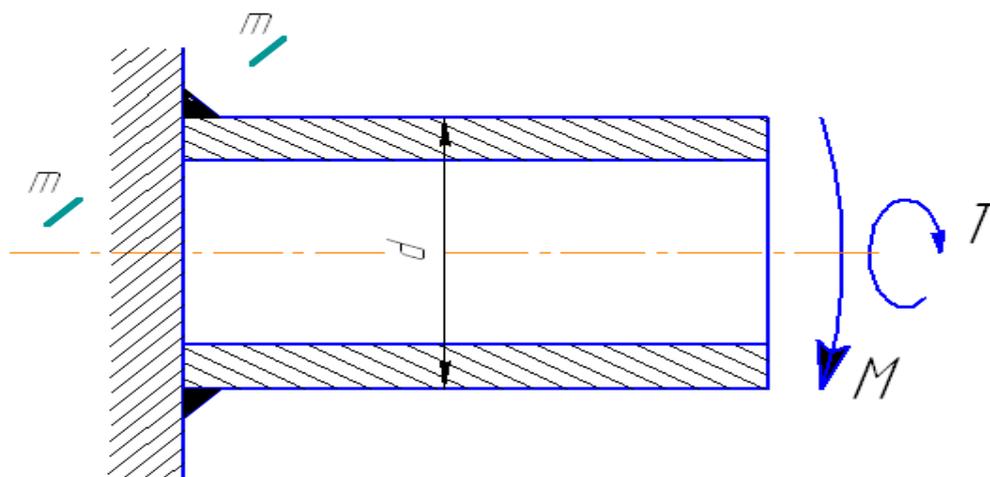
Схема сварного соединения хомутика с действующими нагрузками
